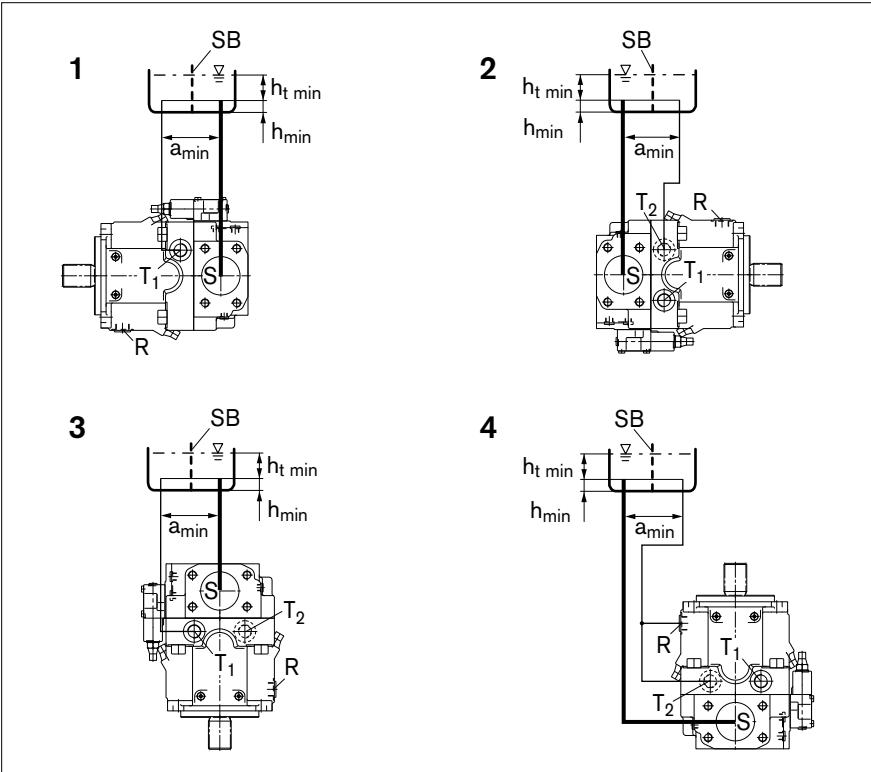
Untertankeinbau mit Einbaulage 1–4
